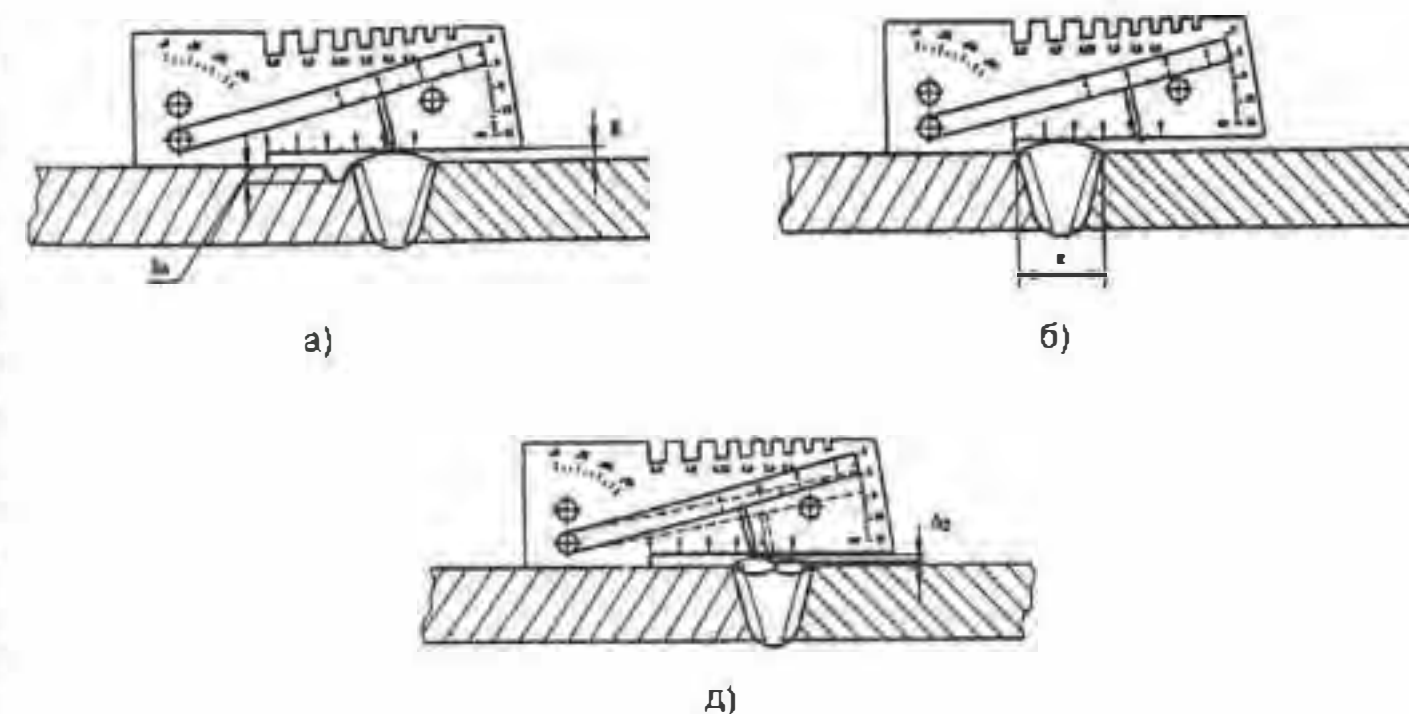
Измерение с помощью шаблона УШС размеров сварного шва
